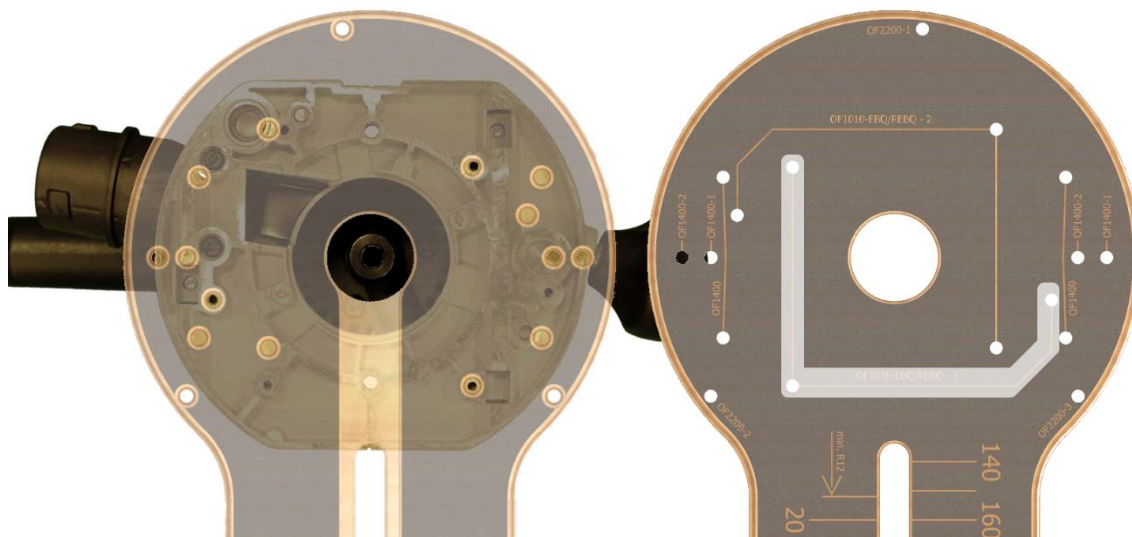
Trous de montage 1 adaptés à Festool OF1010-REBQ
